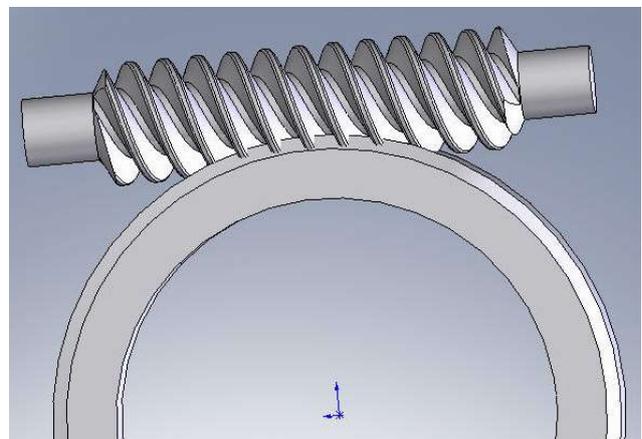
Модели червяка и заготовки червячного колеса в рабочем положении
